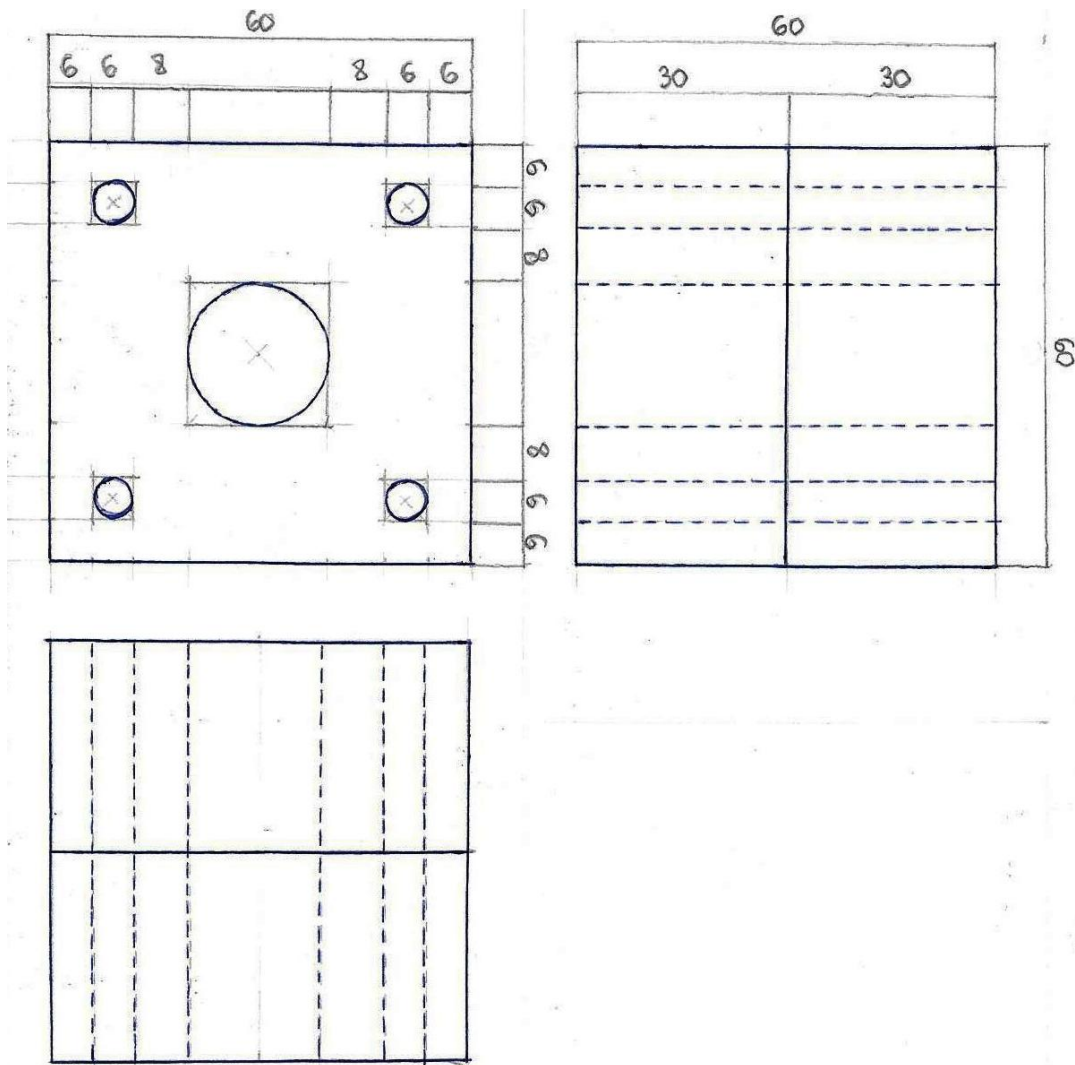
Vistas acotadas (Alzado – Planta – Perfil izqdo.)
